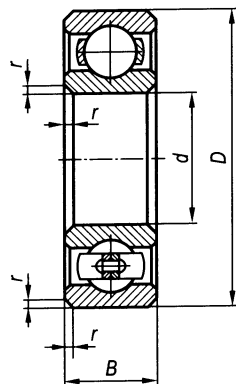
Подшипник шариковый радиальный однорядный
